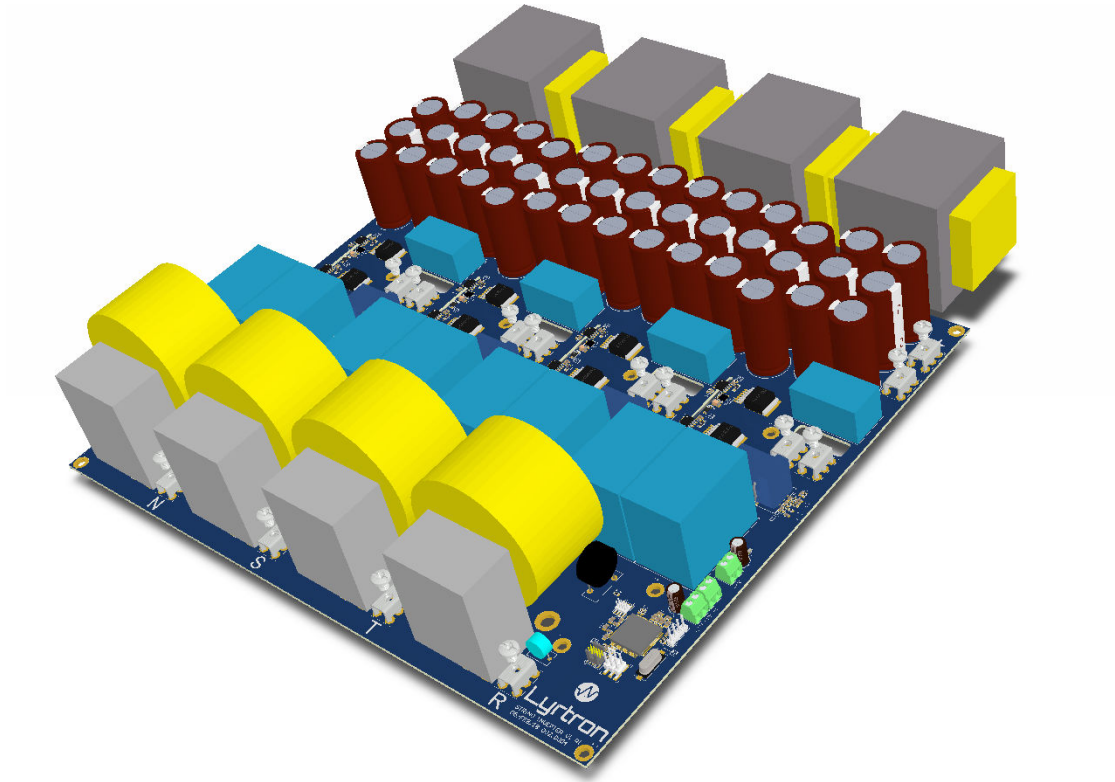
PCB del prototipo fabricado, sus dimensiones son de 26 cm x 30 cm x 5 cm
